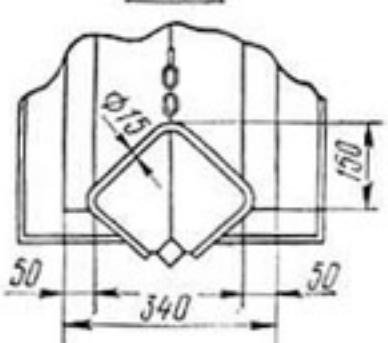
Конструкция сменного цельнометаллического сварного лотка к ЭТЦ-202А для укладки керамических труб с пластмассовыми соединительными муфтами:
